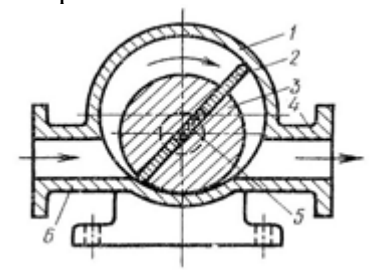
Пластинчатый насос: 1 - корпус; 2 - лопасти; 3 - ротор; 4 - нагнетательный патрубок; 5 - пружина; 6 - всасывающий (приемный) патрубок.
